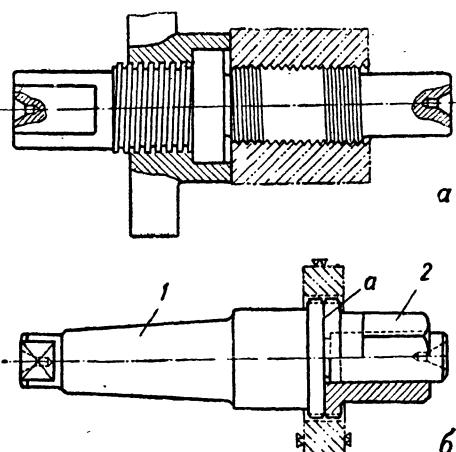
Центровая гезьбовая оправка и оправка для подрезки торцов у гаек.
